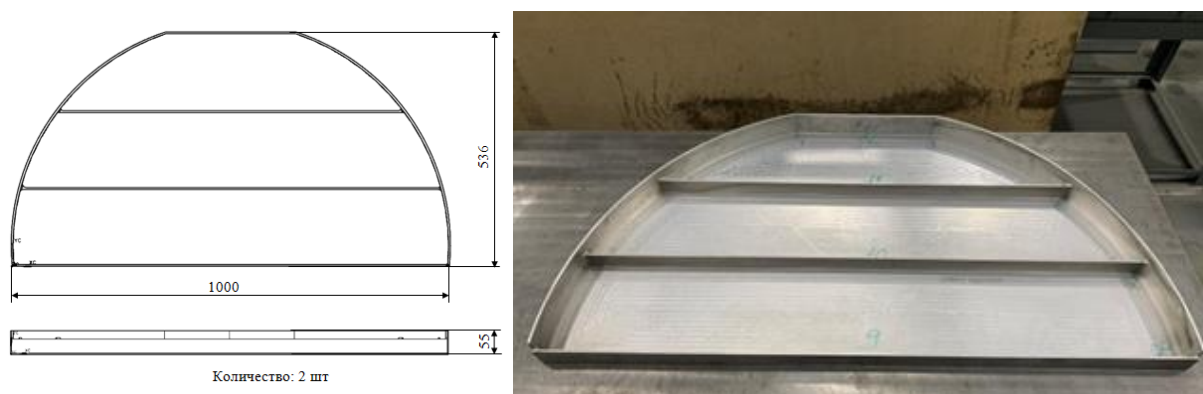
Конструктивно-подобный образец детали «Стенка»
